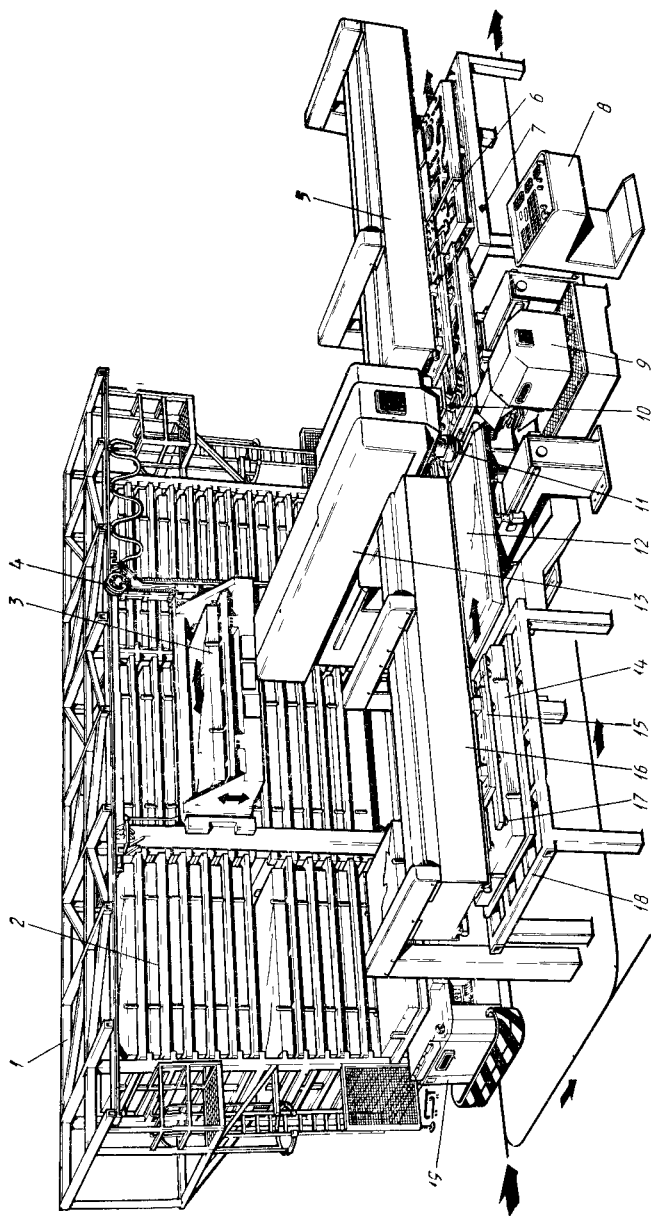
Обрабатывающий центр с ЧПУ фирмы TRUMPF
